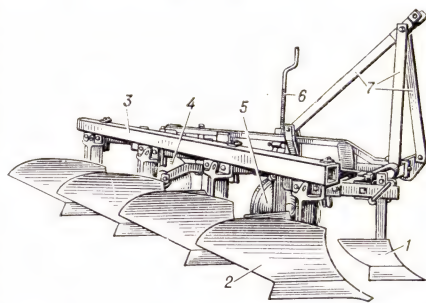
Навесной тракторный плуг: 1 — предплужник; 2 — корпус; 3 — рама; 4 — дисковый нож; 5 — опорное колесо; 6 — винтовой механизм регулирования глубины пахоты; 7 — навеска плуга.
